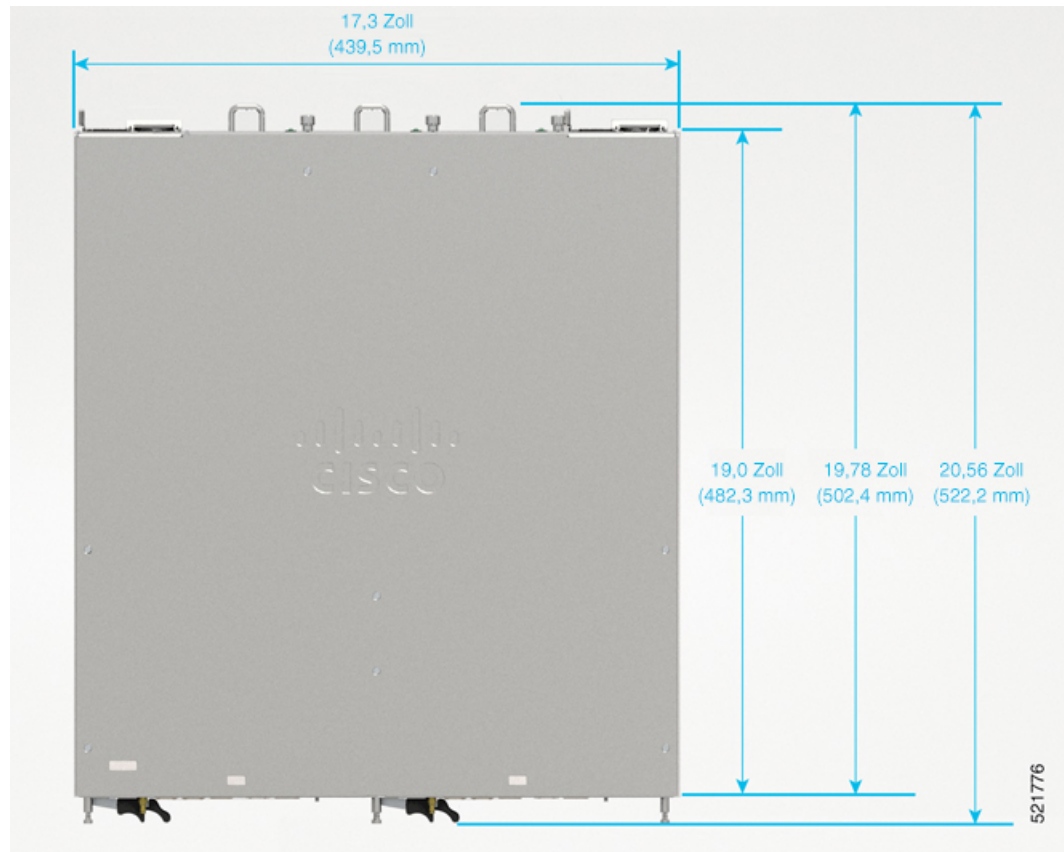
Platzbedarf und Abmessungen des Chassis für den Cisco ASR 9901-Router – Draufsicht
